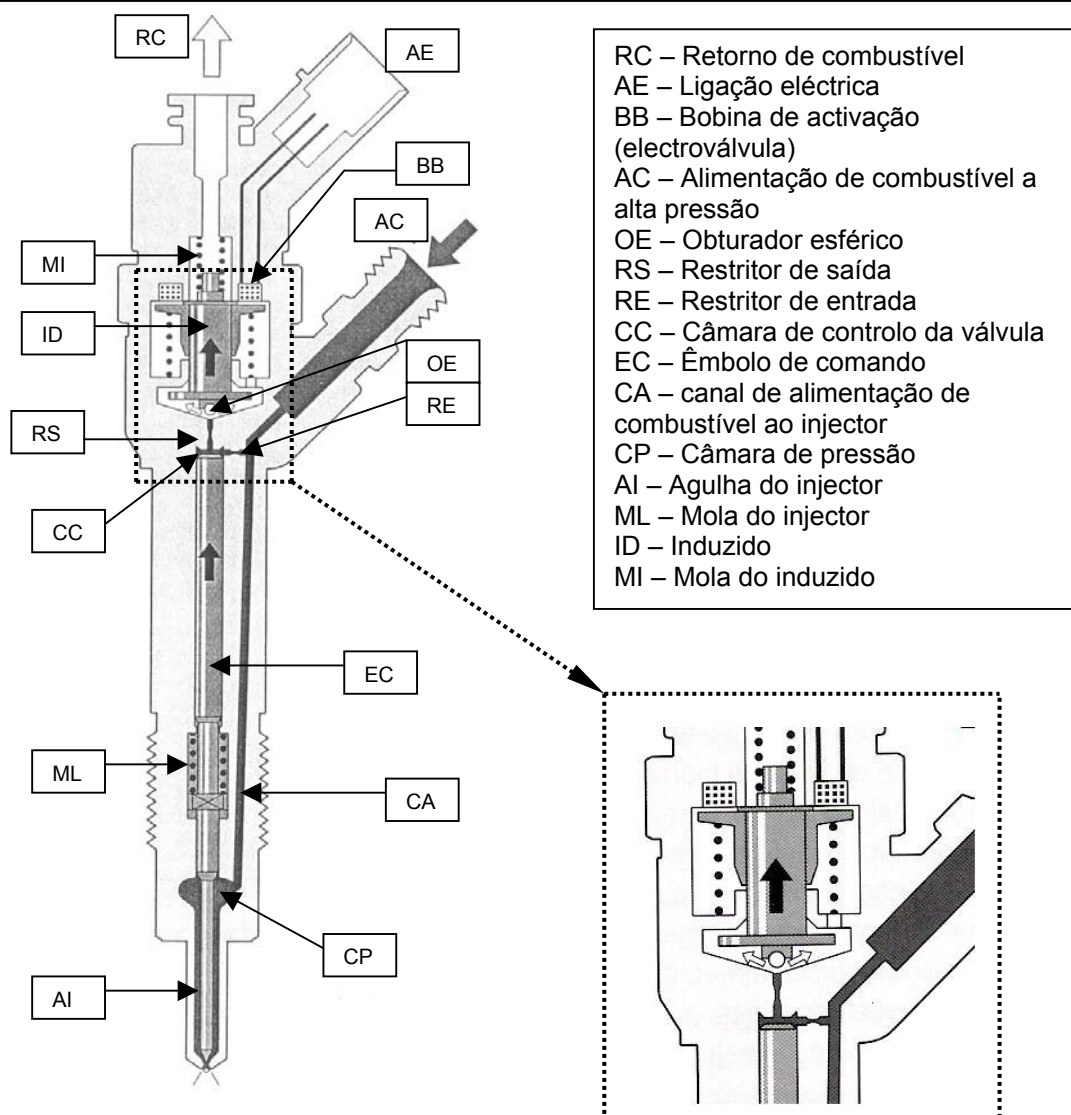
Vista em corte e pormenor de um injetor indutivo
